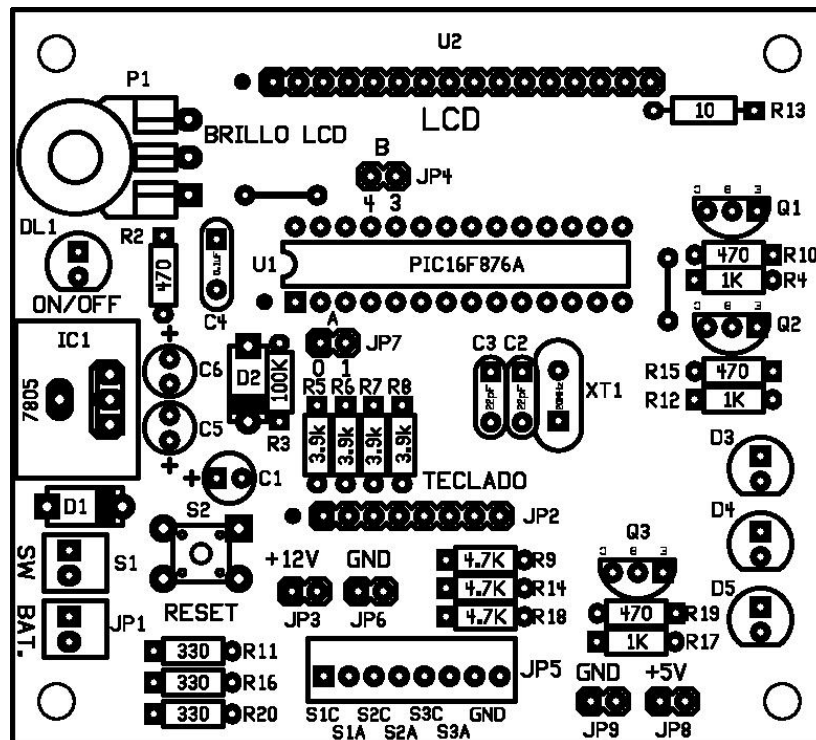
Placa vista desde la parte superior sin elementos soldados.
